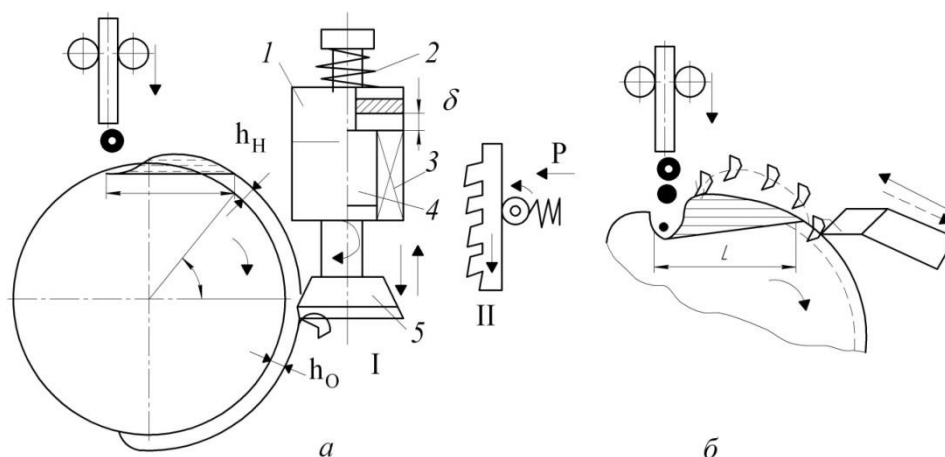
Схемы терморезания: а - резцом (I), протяжкой (II): 1 - статор; 2 - пружина; 3 - обмотка; 4 - якорь; 5 - резец; б - безотходное строгание
